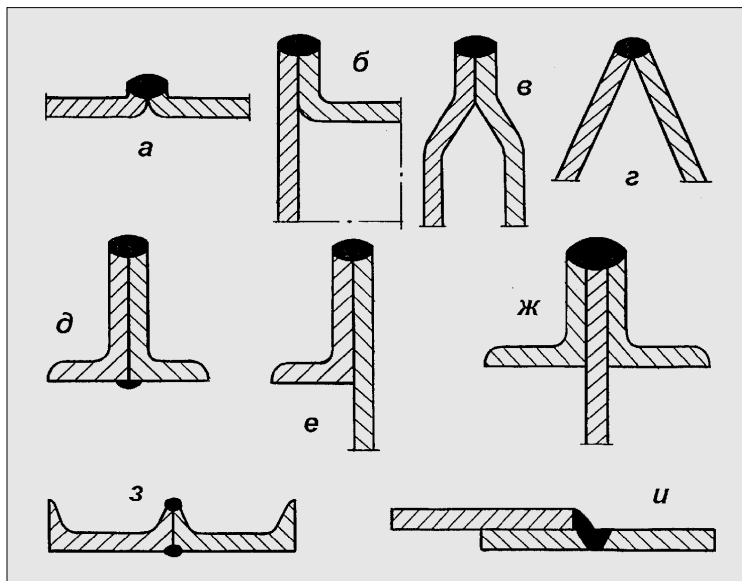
Пример использования сварки без присадочного материала: а - стыковое соединение листов толщиной 1-2 мм с отбортовкой кромок; б - присоединение штампованного днища к обечайке; в - соединение кожухов, емкостей и т. п.; г - угловое соединение; д, е, ж, з - различные виды соединений из уголков, швеллеров и листов, соединение внахлест
